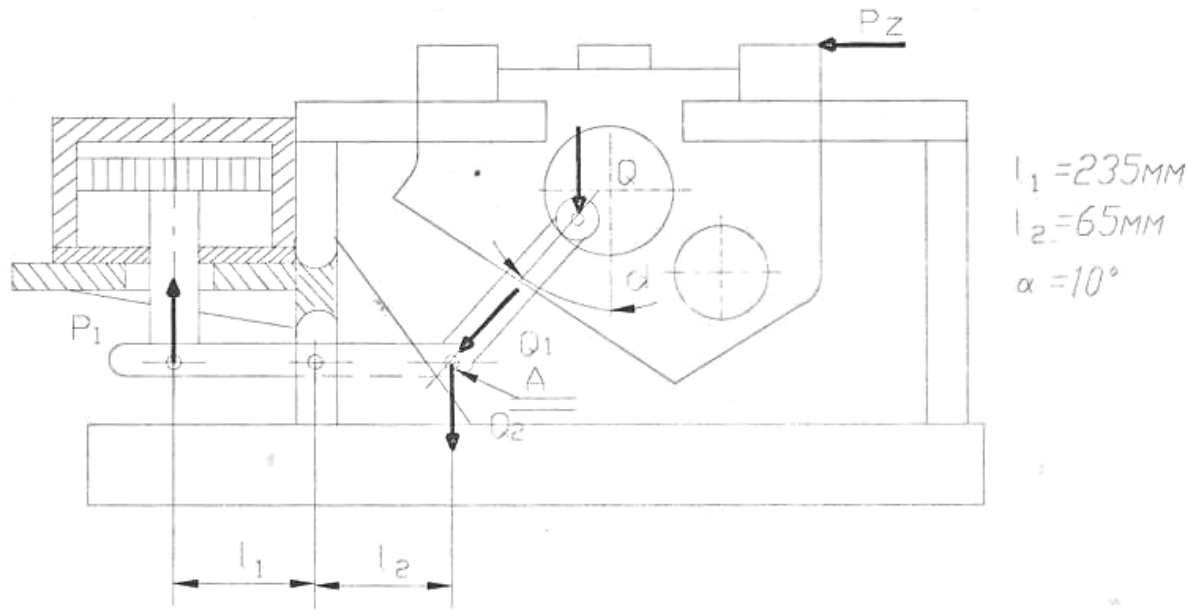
Розрахункова схема пристосування для фрезерування для розрахунку зусилля затиску заготовки.
